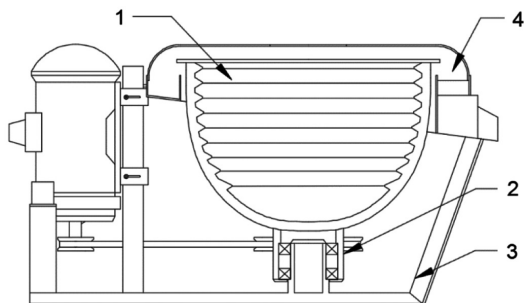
Безнапорный центробежный концентратор: 1 – рабочий орган в виде чаши; 2 – приводной вал с системой подшипников; 3 – несущая рама; 4 – устройство загрузки и разгрузки продуктов обогащения
